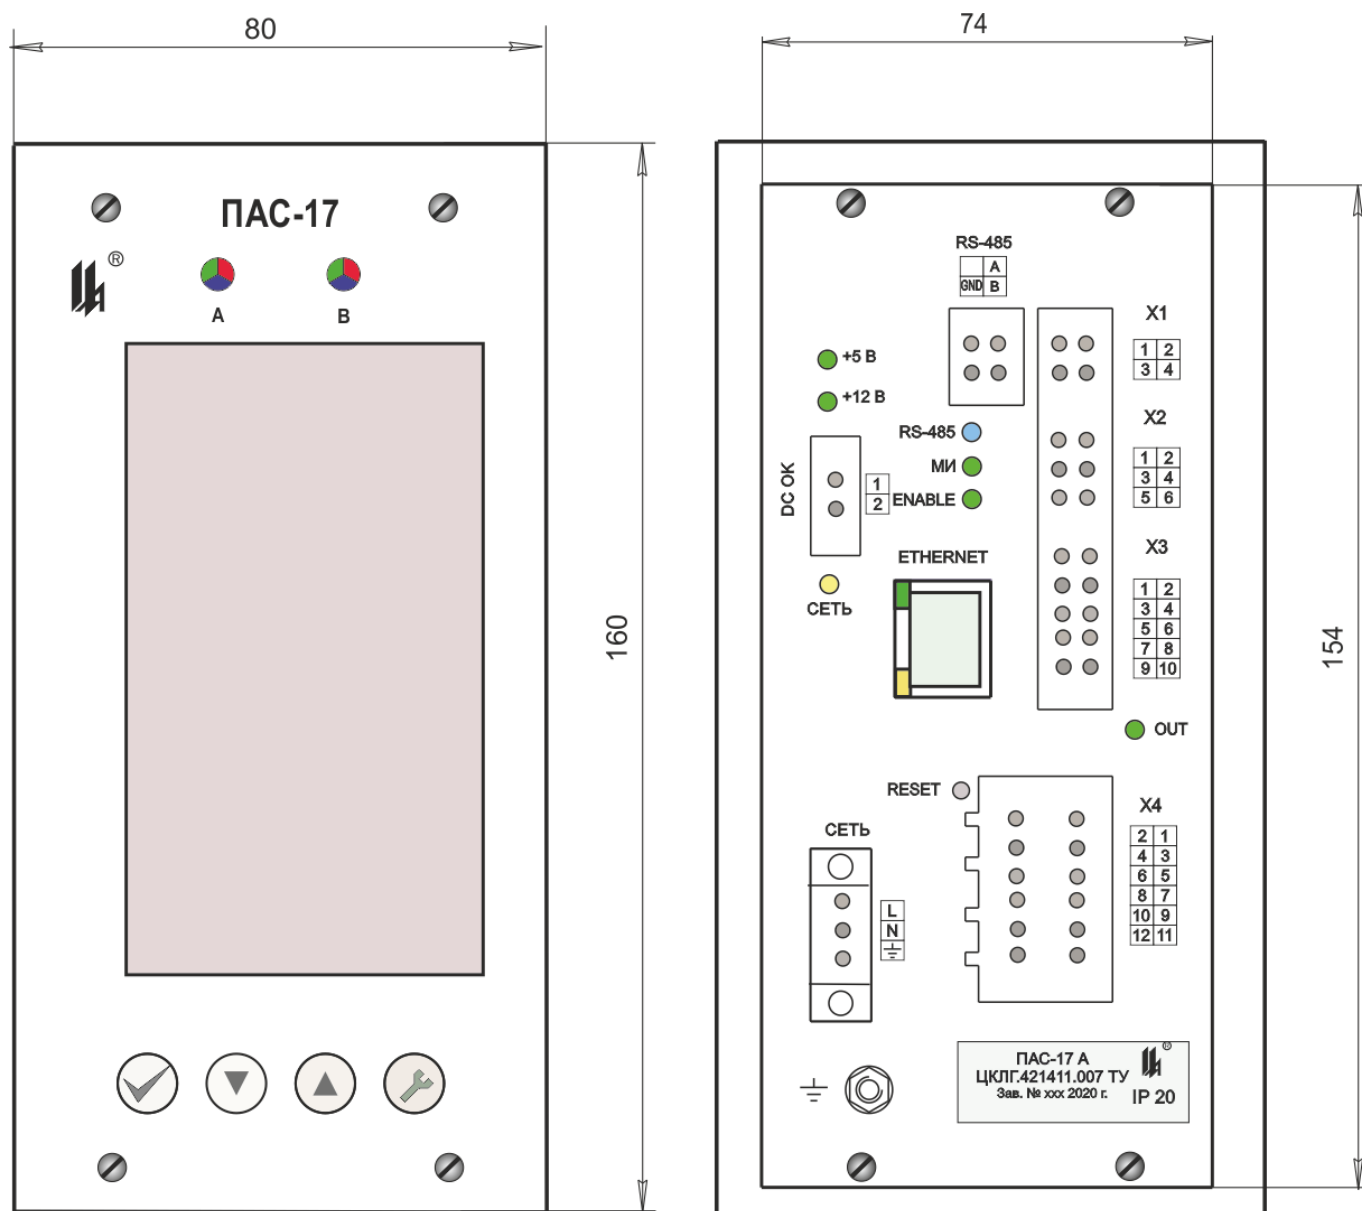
Внешний вид и габаритные размеры ПАС-17А
